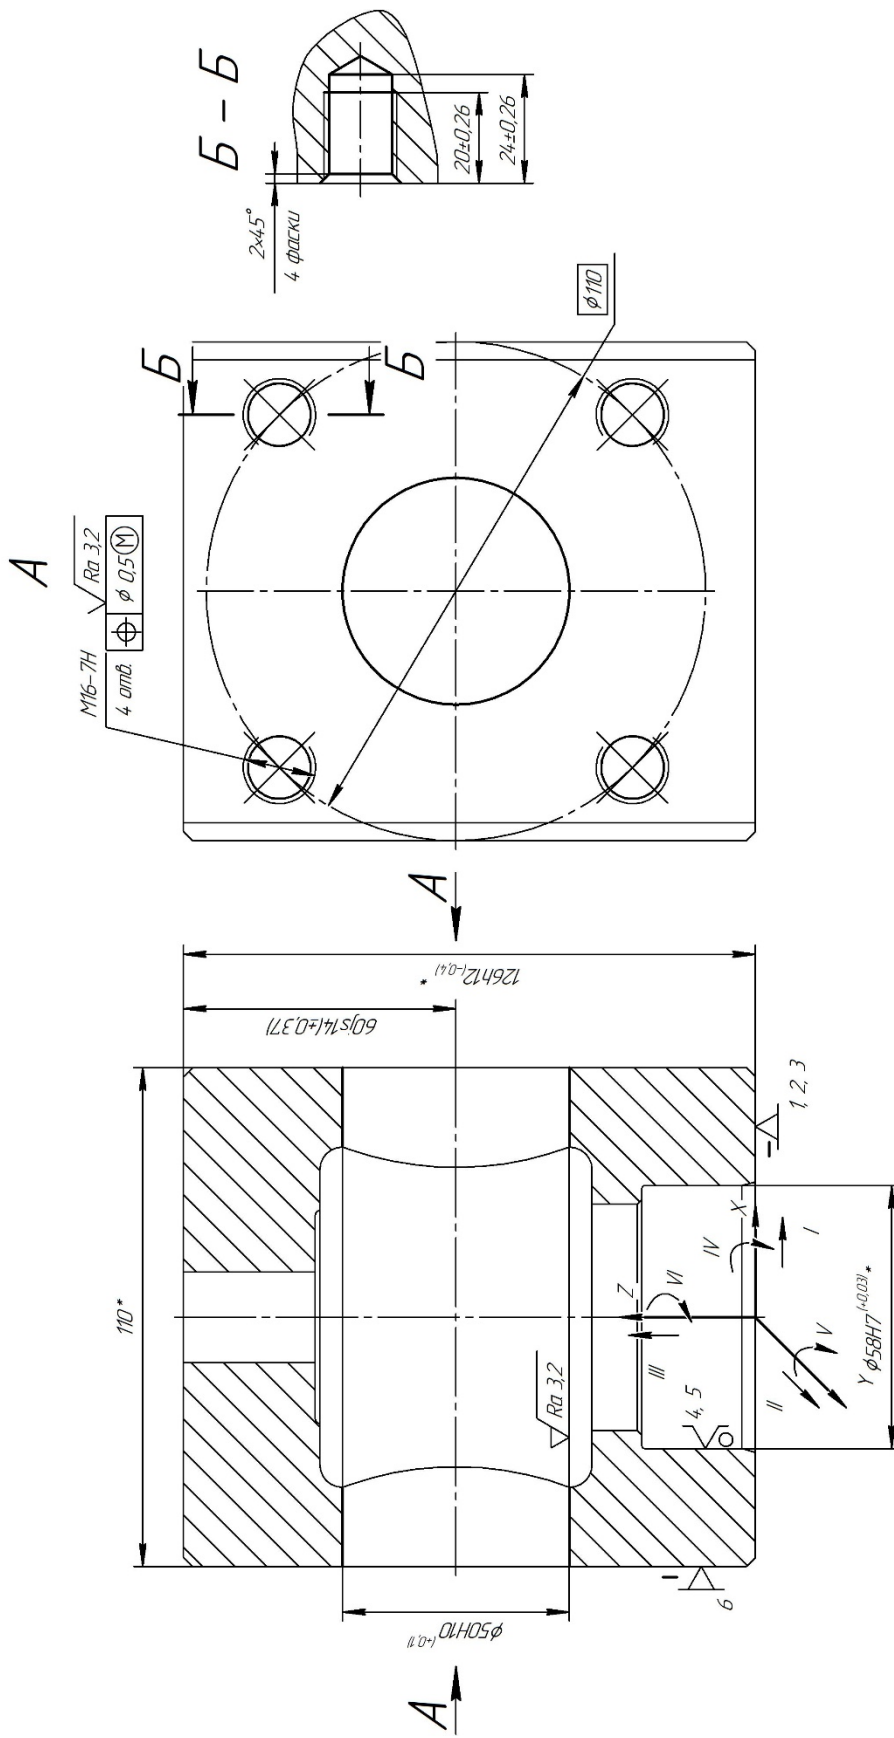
Схема базування й закріплення заготовки на операції 040
